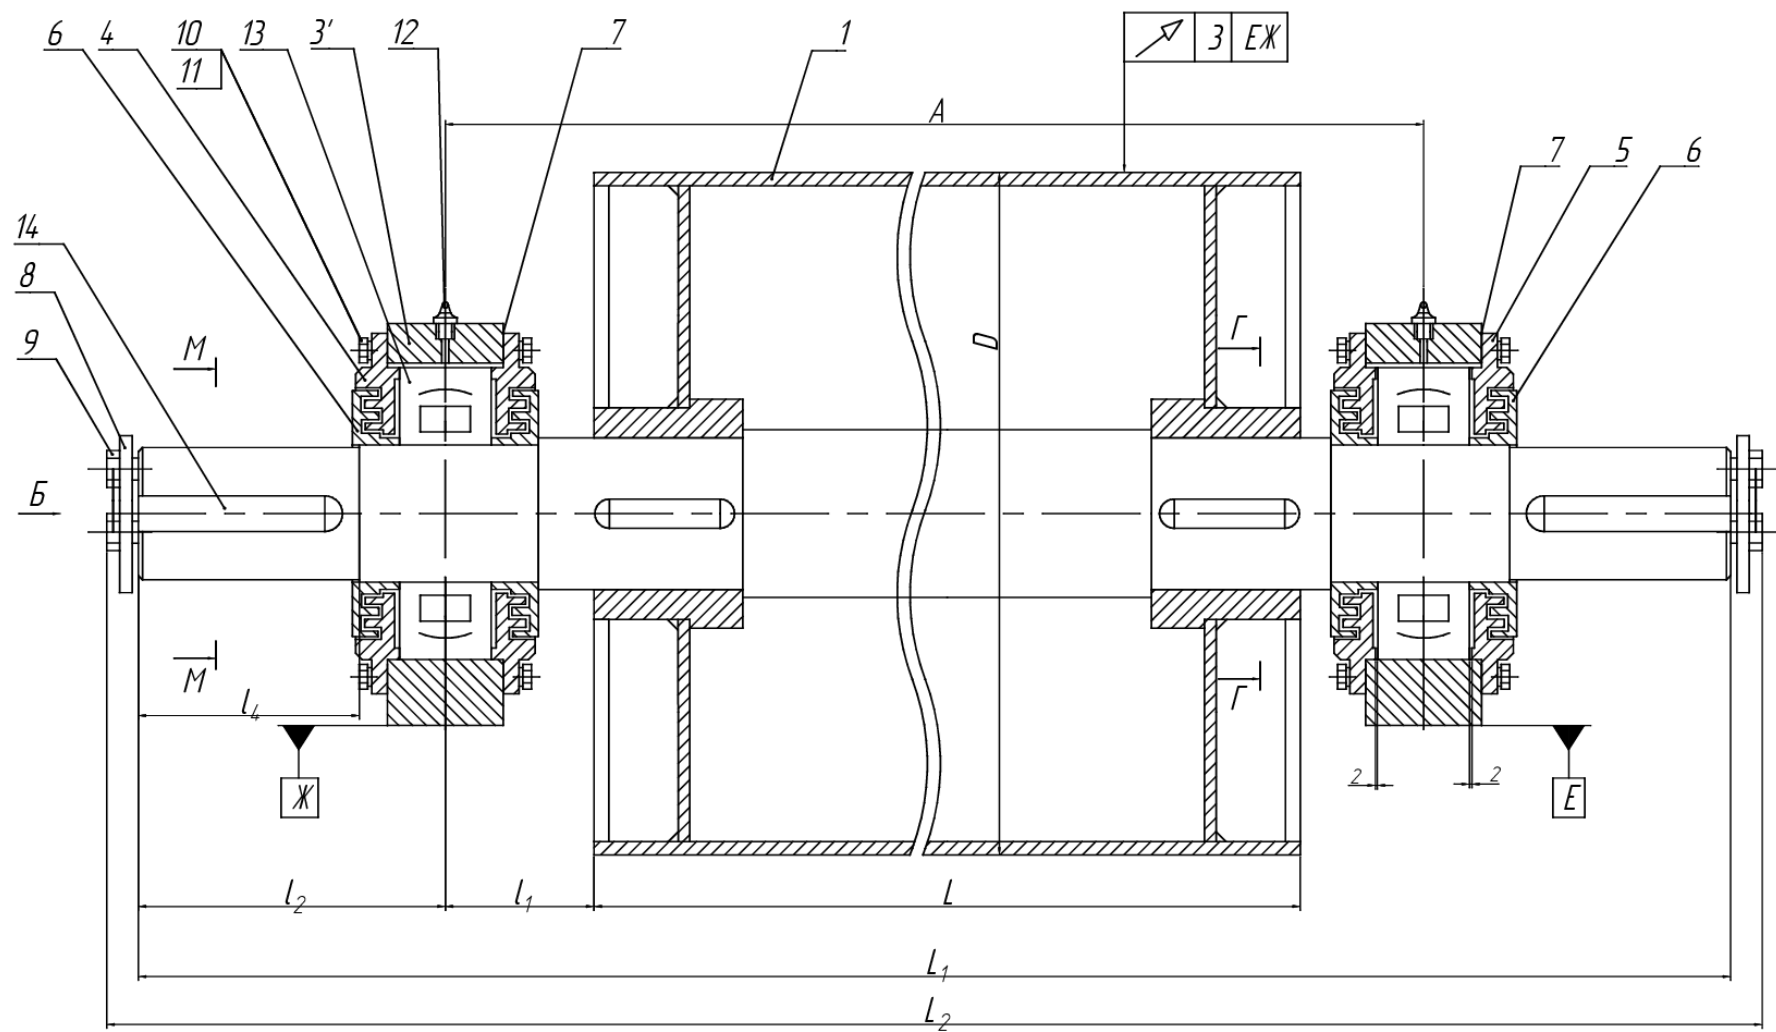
Барабан ленточного конвейера для ленты шириной 0,8 – 1,0 м конструкции ОАО «ОМТ»
